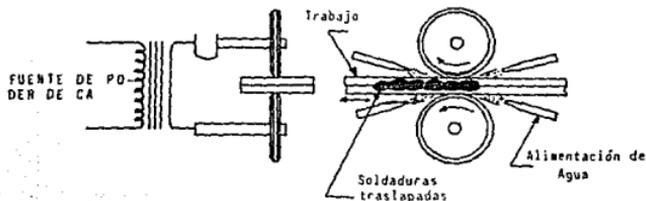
Representación esquemática de soldadura de costura.
